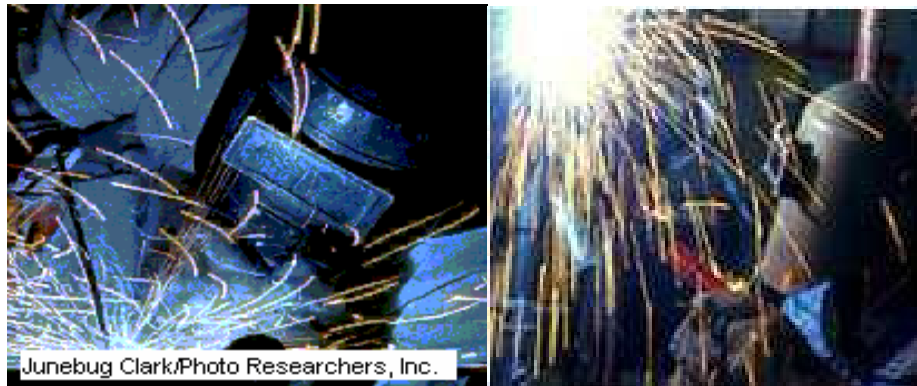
Soldadura metálica con arco protegido (soldadura de varilla) ejecutada por un soldador
